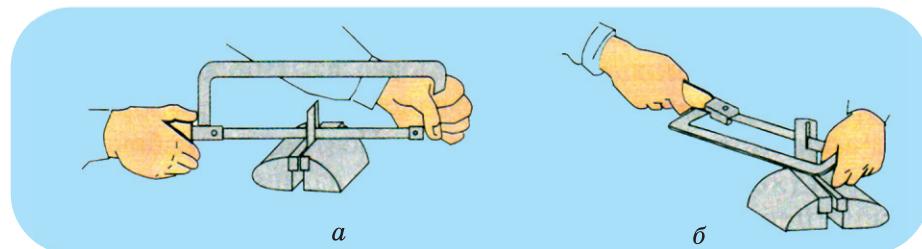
Работа ножовкой: а) – положение корпуса;
